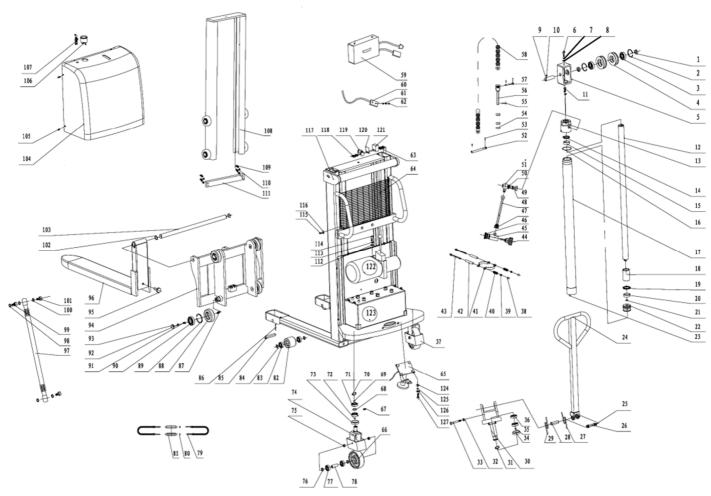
Explosionszeichnung des Hydraulik-Staplers mit Elektroantrieb DYC.
